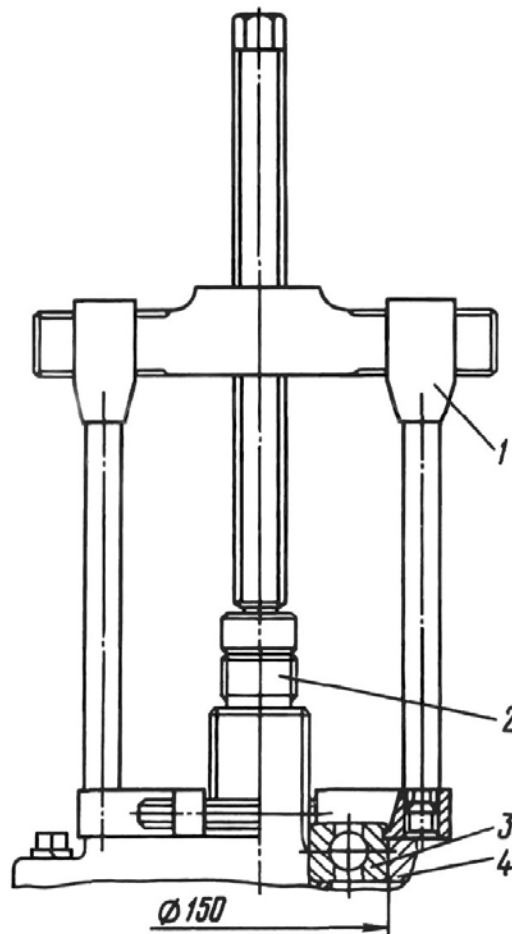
Съёмник для снятия подшипников и шестерен раздаточной коробки:
